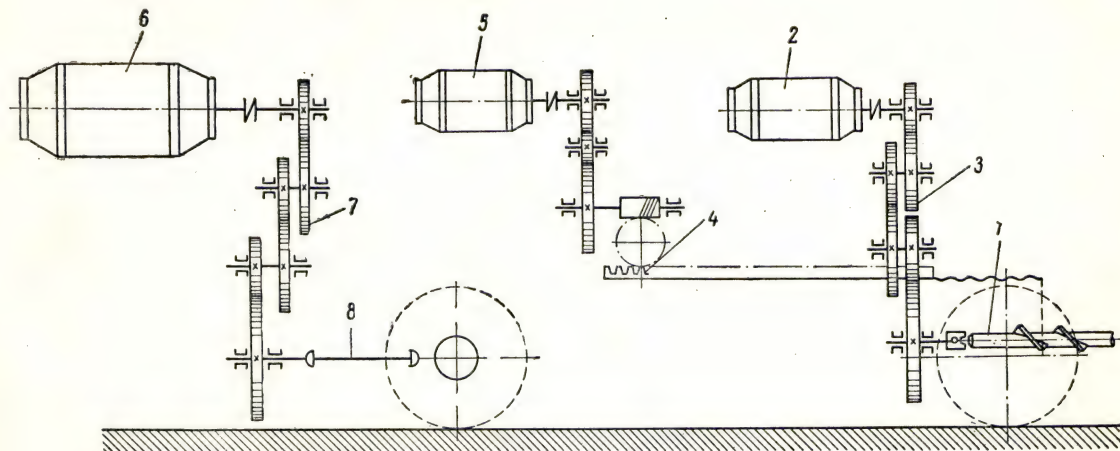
Кинематическая схема бурового станка «Сибиряк»
